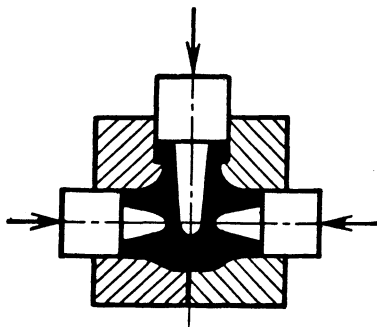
Схема процесса штамповки жидкого металла с трехсторонним прессованием
